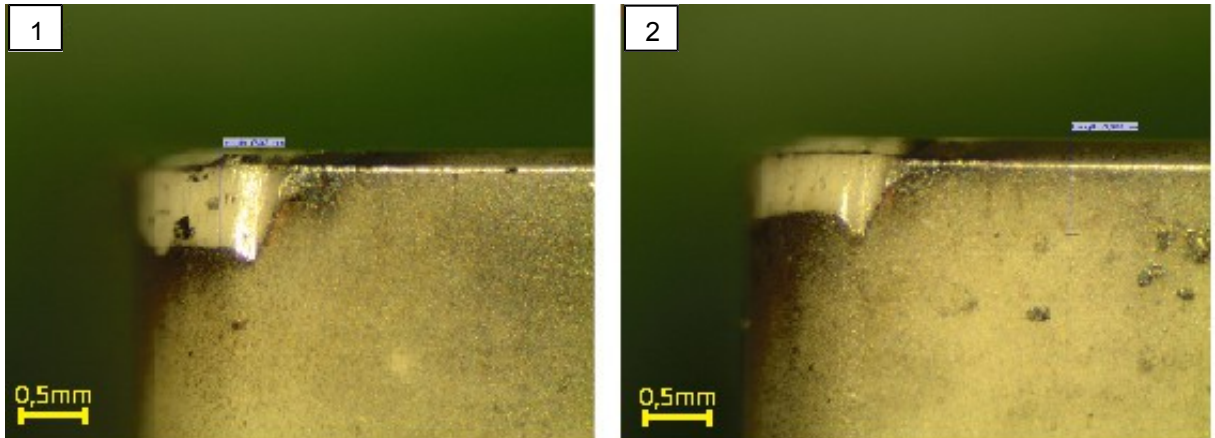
Desgaste de flanco da $V_c = 200$ m/min, $f = 0,25$ mm/rot; Figura 7- Desgaste de flanco da $V_c = 300$ m/min, $f = 0,25$ mm/rot.
